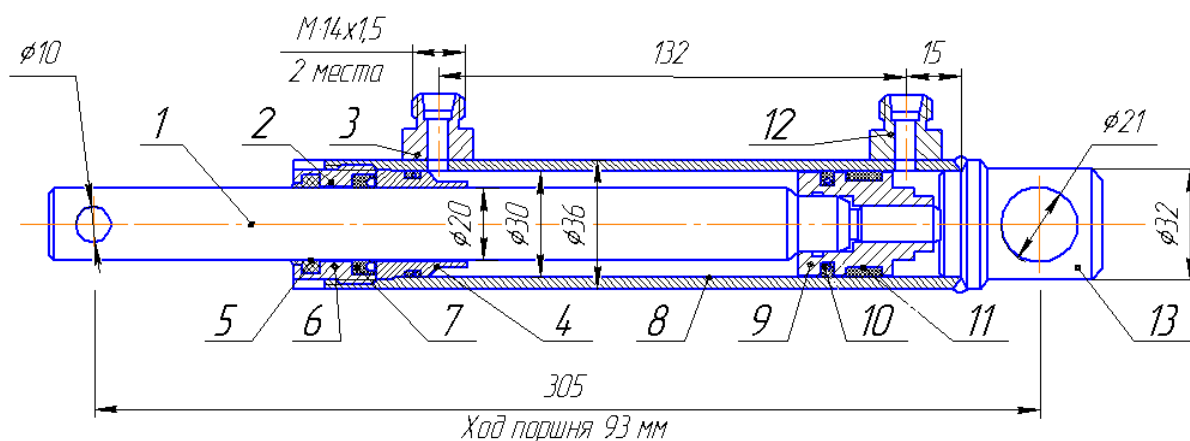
Чертеж гидроцилиндра: 1 – шток; 2 – гайка; 3 – штуцер; 4 – втулка; 5 – грязесъемник; 6 – гайка; 7 – манжета; 8 – корпус гидроцилиндра; 9 – поршень; 10 – манжета; 11 – кольцо; 12 – штуцер; 13 – проушина
